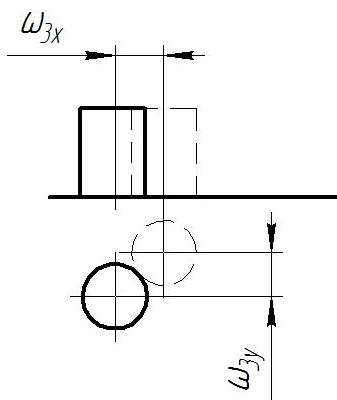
Похибка положення заготовки на проміжних позиціях
